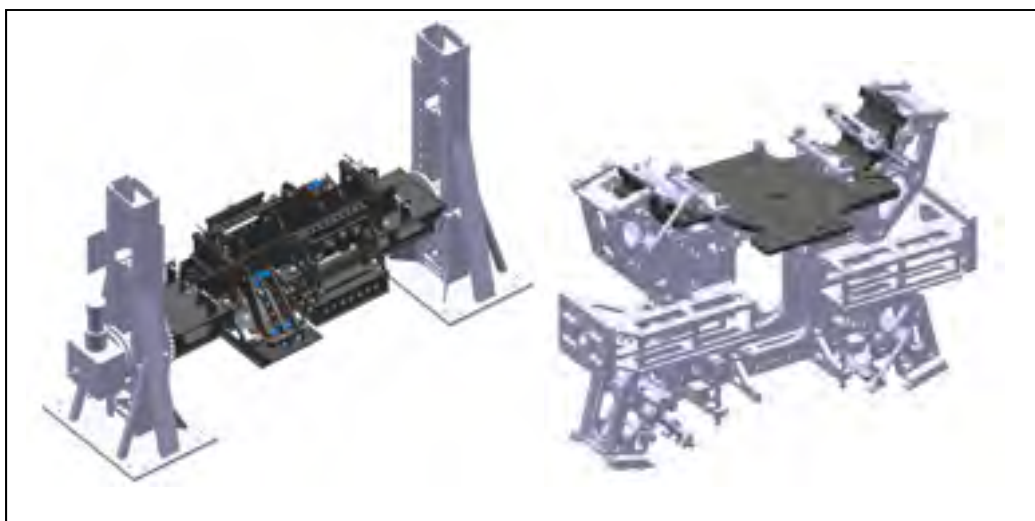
Vues 3D de deux différents outillages d'assemblage pour le soudage
